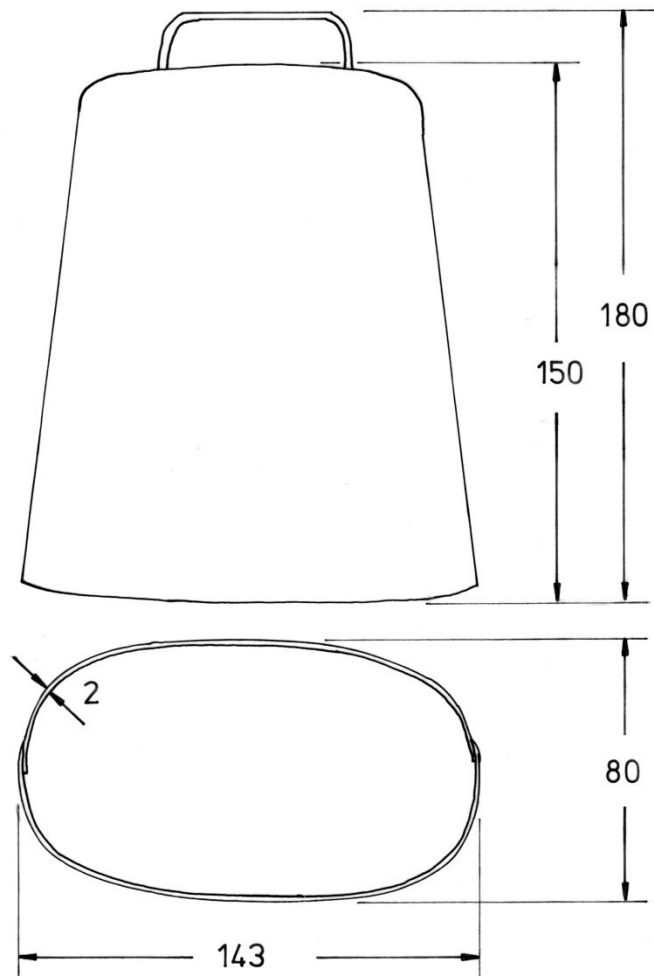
und 54 zeigen, dass der Querschnitt der Glocke im oberen Teil weitgehend rechteckig ist. Zur Öffnung hin wird er annähernd elliptisch, wie der unteren Ansicht in Fig. 53 zu entnehmen ist. Die äußere Geometrie der Glocke weicht damit extrem von der Rotationssymmetrie ab. Dies gilt auch für die Wanddicke. Im Bereich der Schweißnähte an den Schmalseiten verdoppeln Überlappungen die Wanddicke auf eine Länge von etwa 10 mm.
